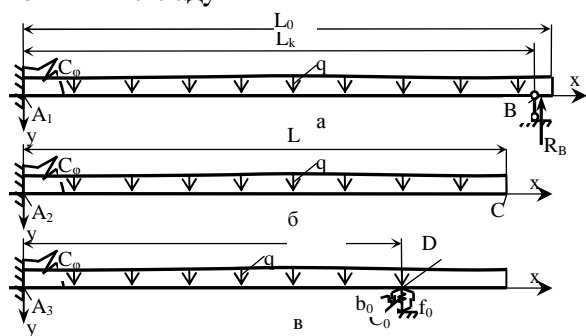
Зміна умов опирання і закріплення заготовки, яка має місце при роботі верстата: а – опирання кінцевої частини заготовки на кільце; б – консольне закріплення заготовки; в – введення проміжної пружно-демпфуючої опори заготовки
